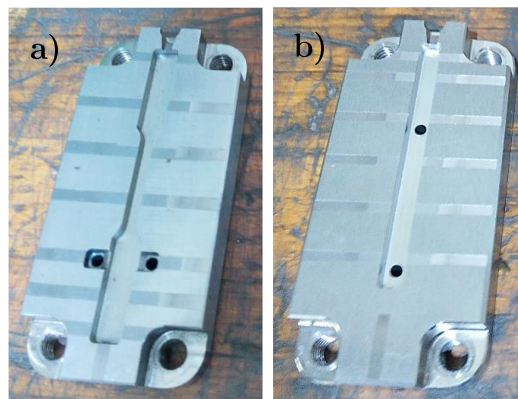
Equipamento usado para injeção dos provetes (Mariteste - Injeção e Produção de Plásticos Técnicos Lda)
